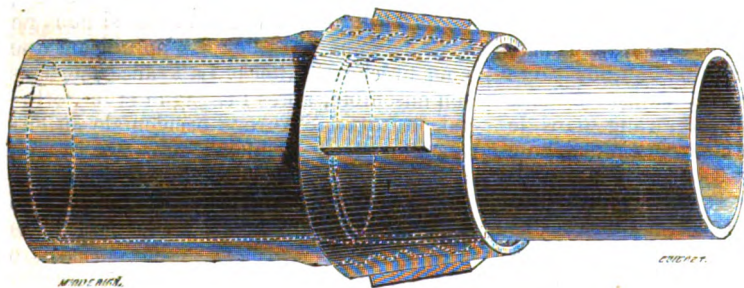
Joint mobile de M. Gandillot assemblant un tube flexible avec un tube rigide.
